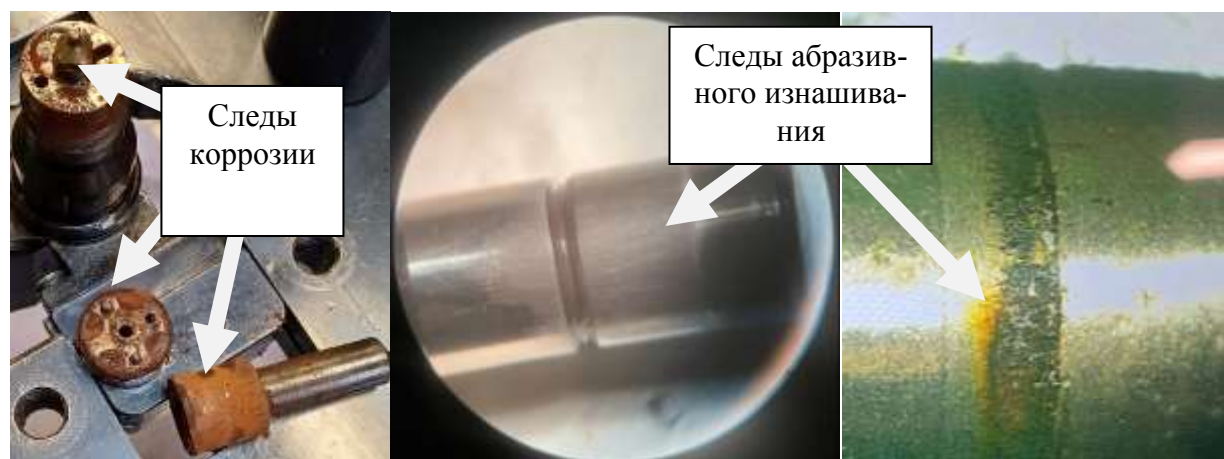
Коррозионный и абразивный износ элементов форсунки
